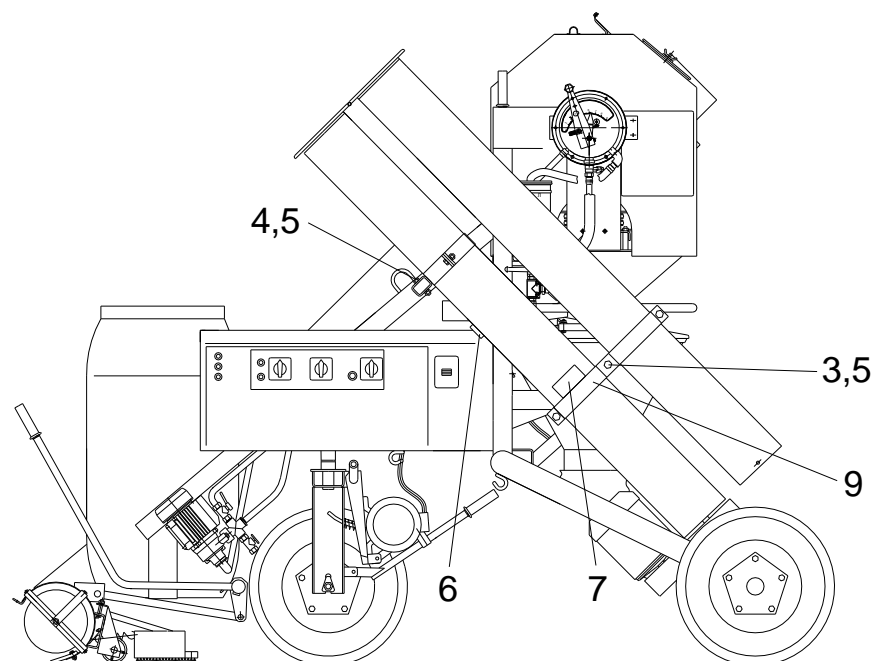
Монтаж вивантажувального шнека на камері протруювання
